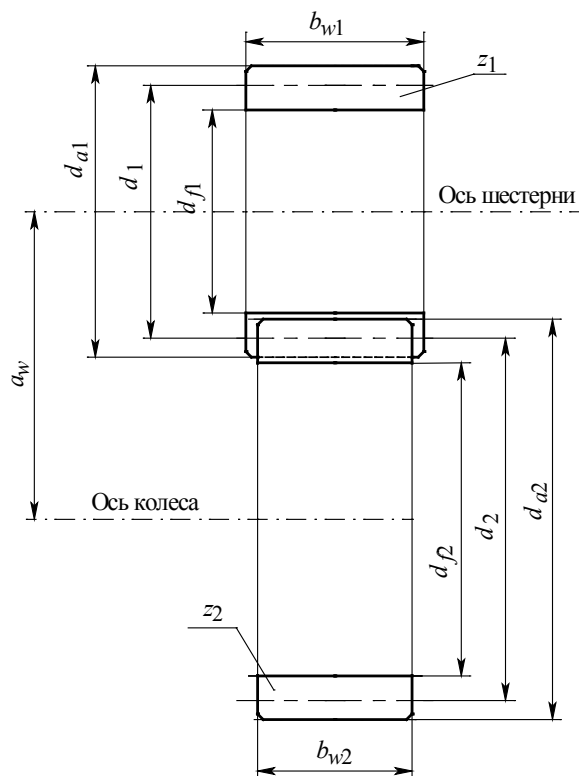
Основные размеры цилиндрической зубчатой передачи.
